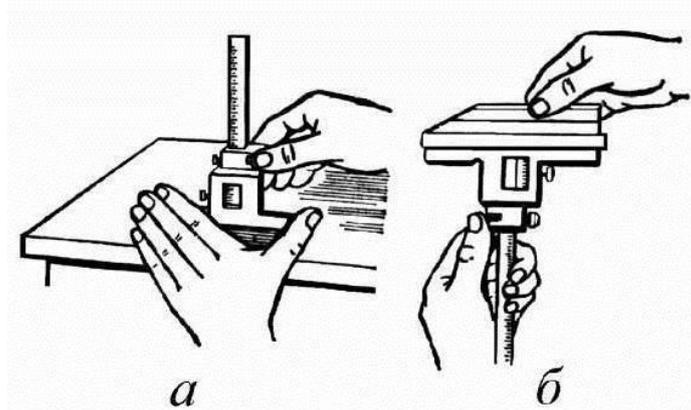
Проверка нулевого положения: а – на поверочной плите, б - лекальной линейкой
